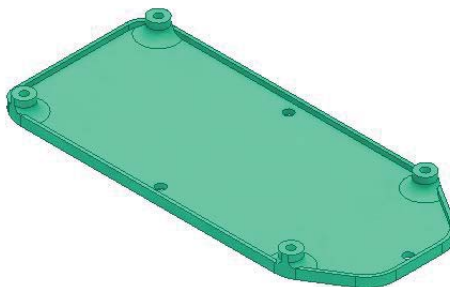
Placa soporte pcb controlador de vuelo y receptor.
